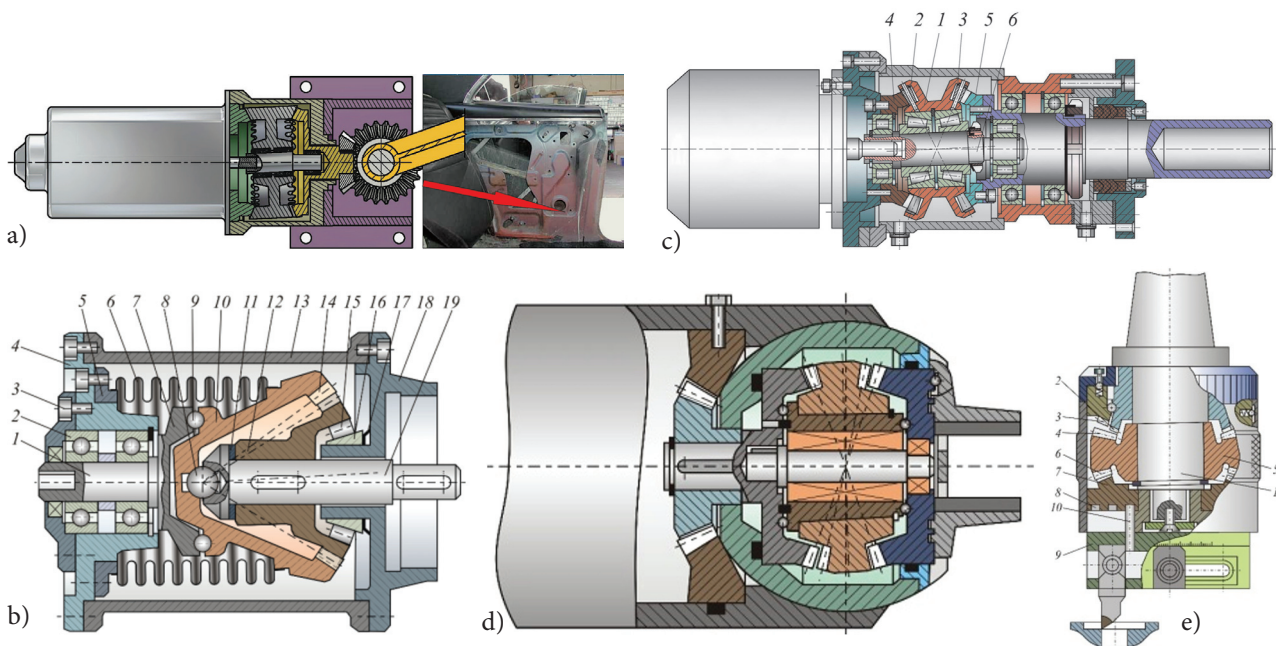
TPP cinematice în: automobile (a), mecanisme ermetice (b), mecanica fină (c), robotehnică (d), utilaje și mecanisme cu destinație generală și specială (e)
